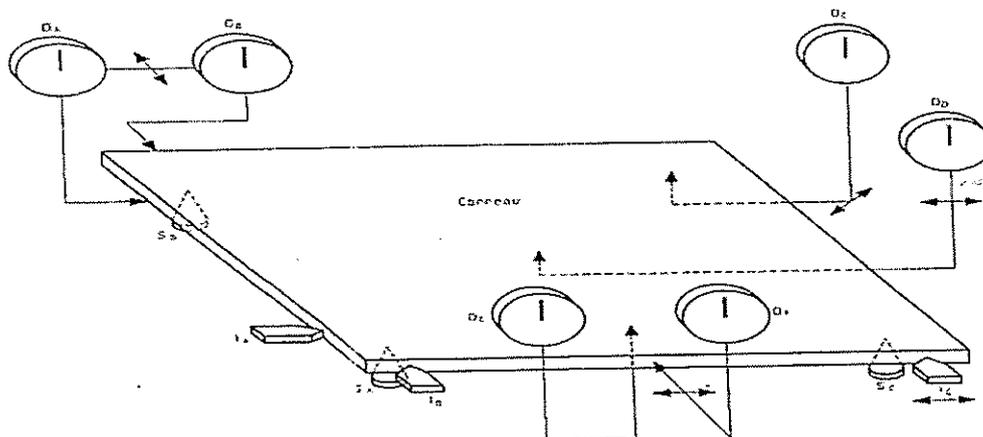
Dispositif pour le mesurage de la rectitude des arêtes, de l'angularité et de la planéité de surface
